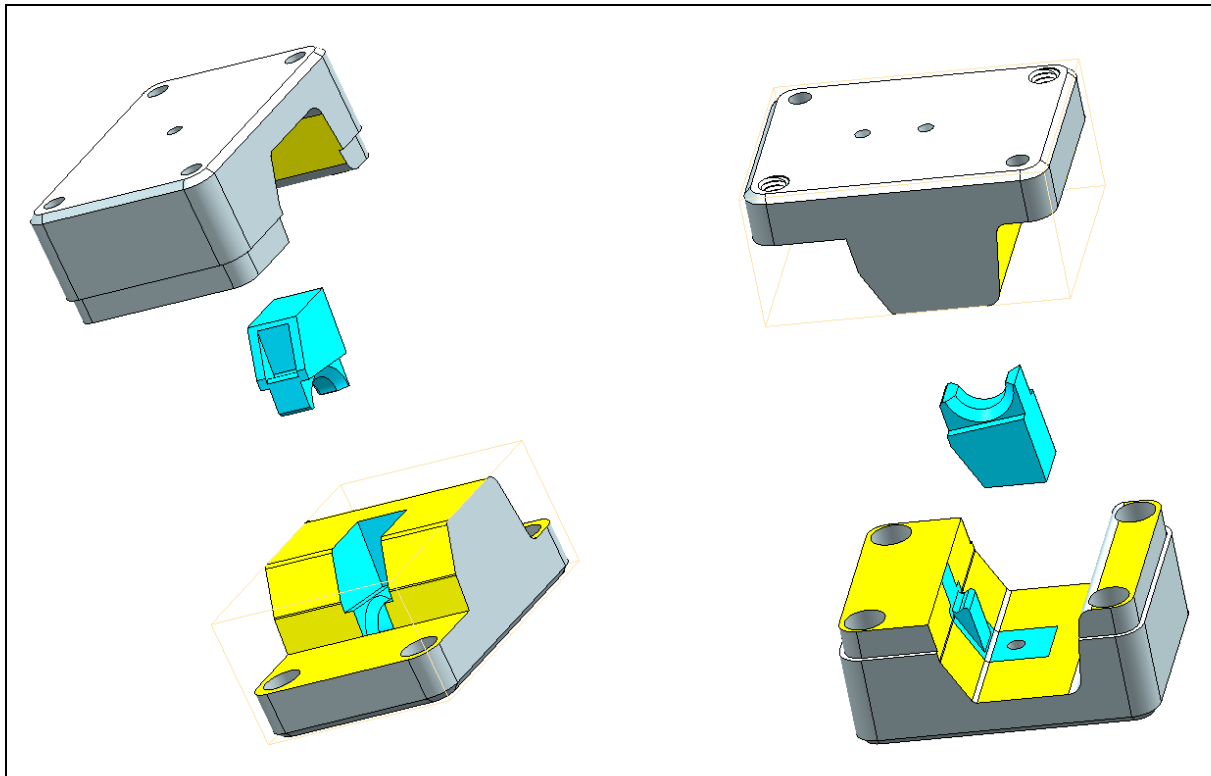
CAD-Modell: erstes ungehärtetes Spritzgusswerkzeug und Spritzling
